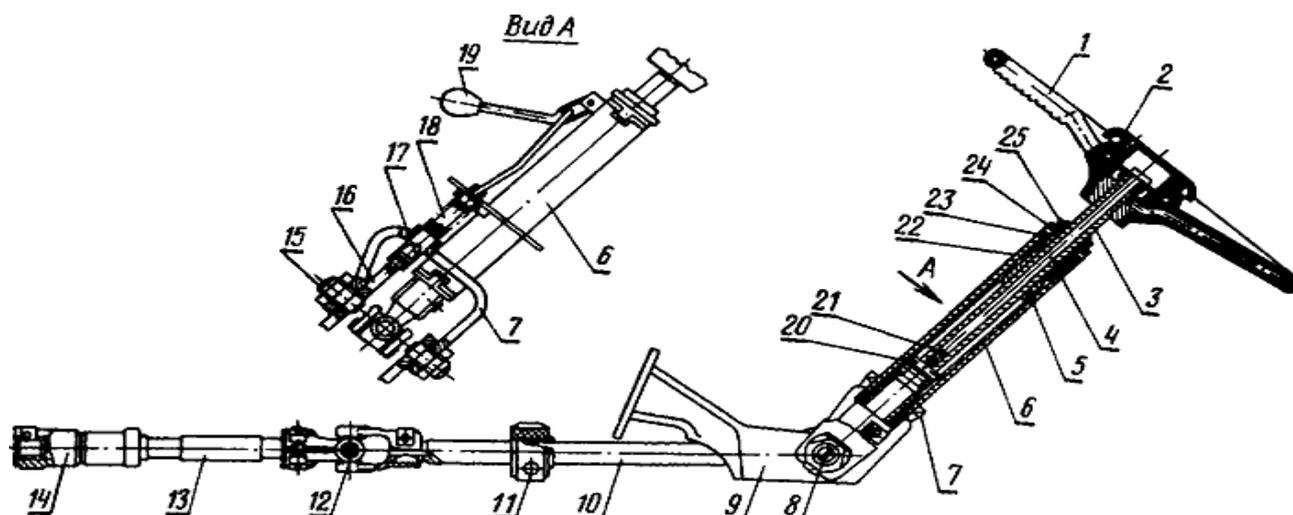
Привод рулевого механизма: 1 - рулевое колесо; 2 - маховичок; 3 - рулевой вал; 4 - винт; 5 - промежуточный вал; 6 - труба рулевой колонки; 7 - серьга; 8 и 12 - карданные шарниры; 9 - стойка; 10 - средний вал; 11 - промежуточная опора; 13 - передний вал; 14 - шлицевая втулка; 15 - винт; 16 - правая стенка стойки; 17 - фиксатор; 18 - пружина; 19 - рукоятка; 20 - штифт; 21 и 24 - гайка; 22 - втулка; 23 - амортизатор; 25 - контргайка.
